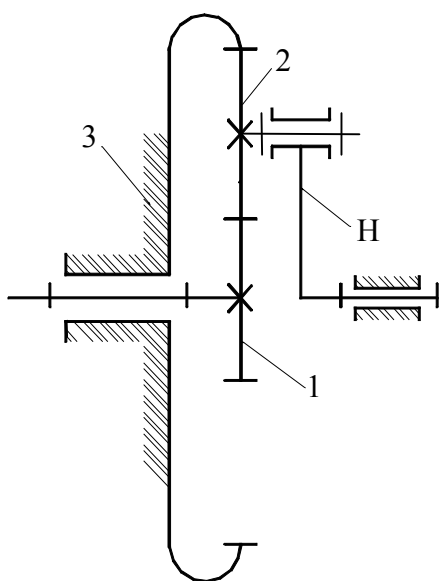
Кінематична схема однорядного планетарного механізму
